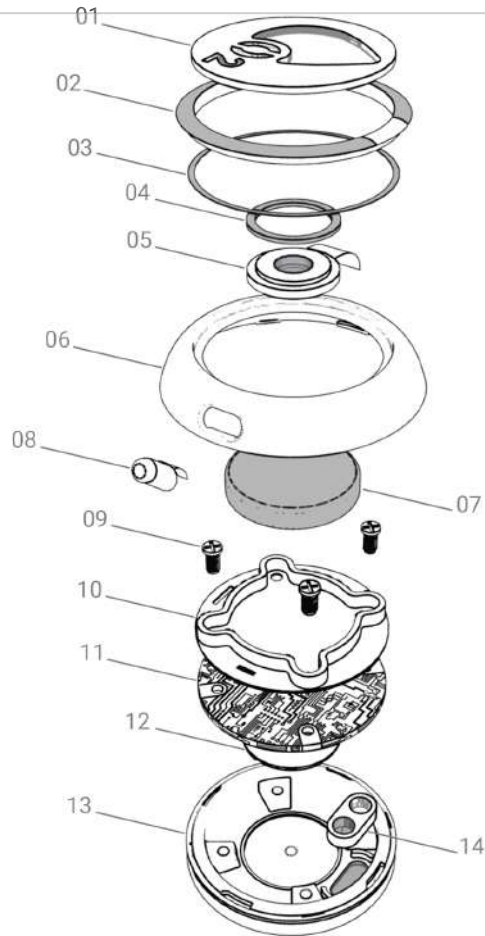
Ilustración explosivo del sensor de oximetría.
